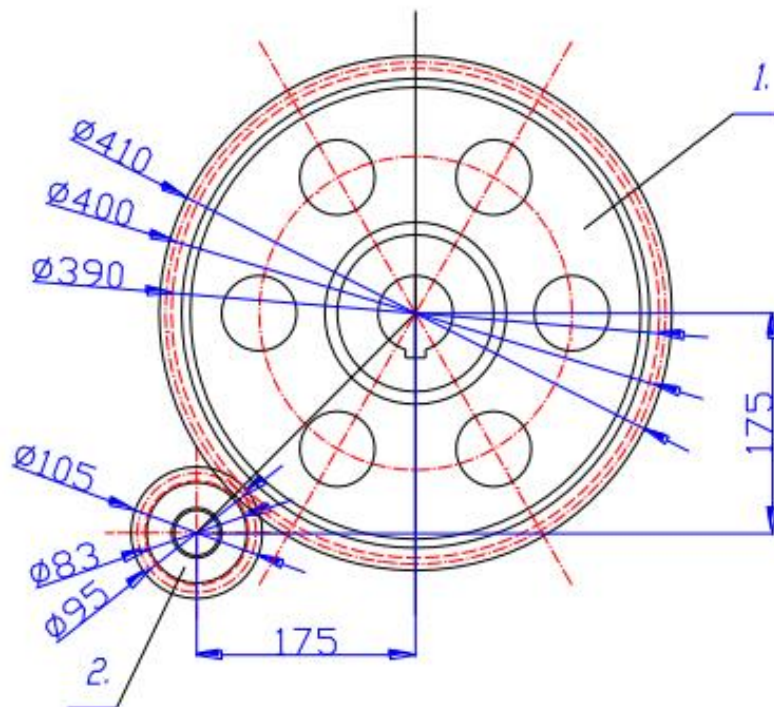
Вузол приводу фаршешішалки марки Л5-ФМБ: 1-зубчасте колесо; 2-вал-шестерня
